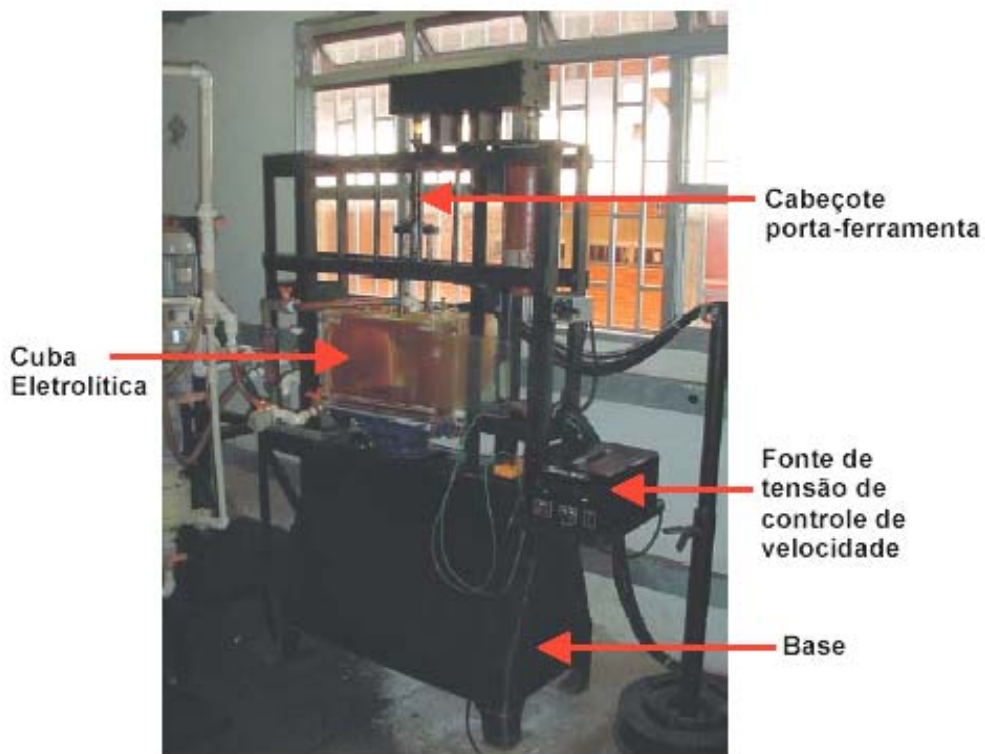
Vista principal do equipamento de usinagem eletroquímica desenvolvido na UFU.
